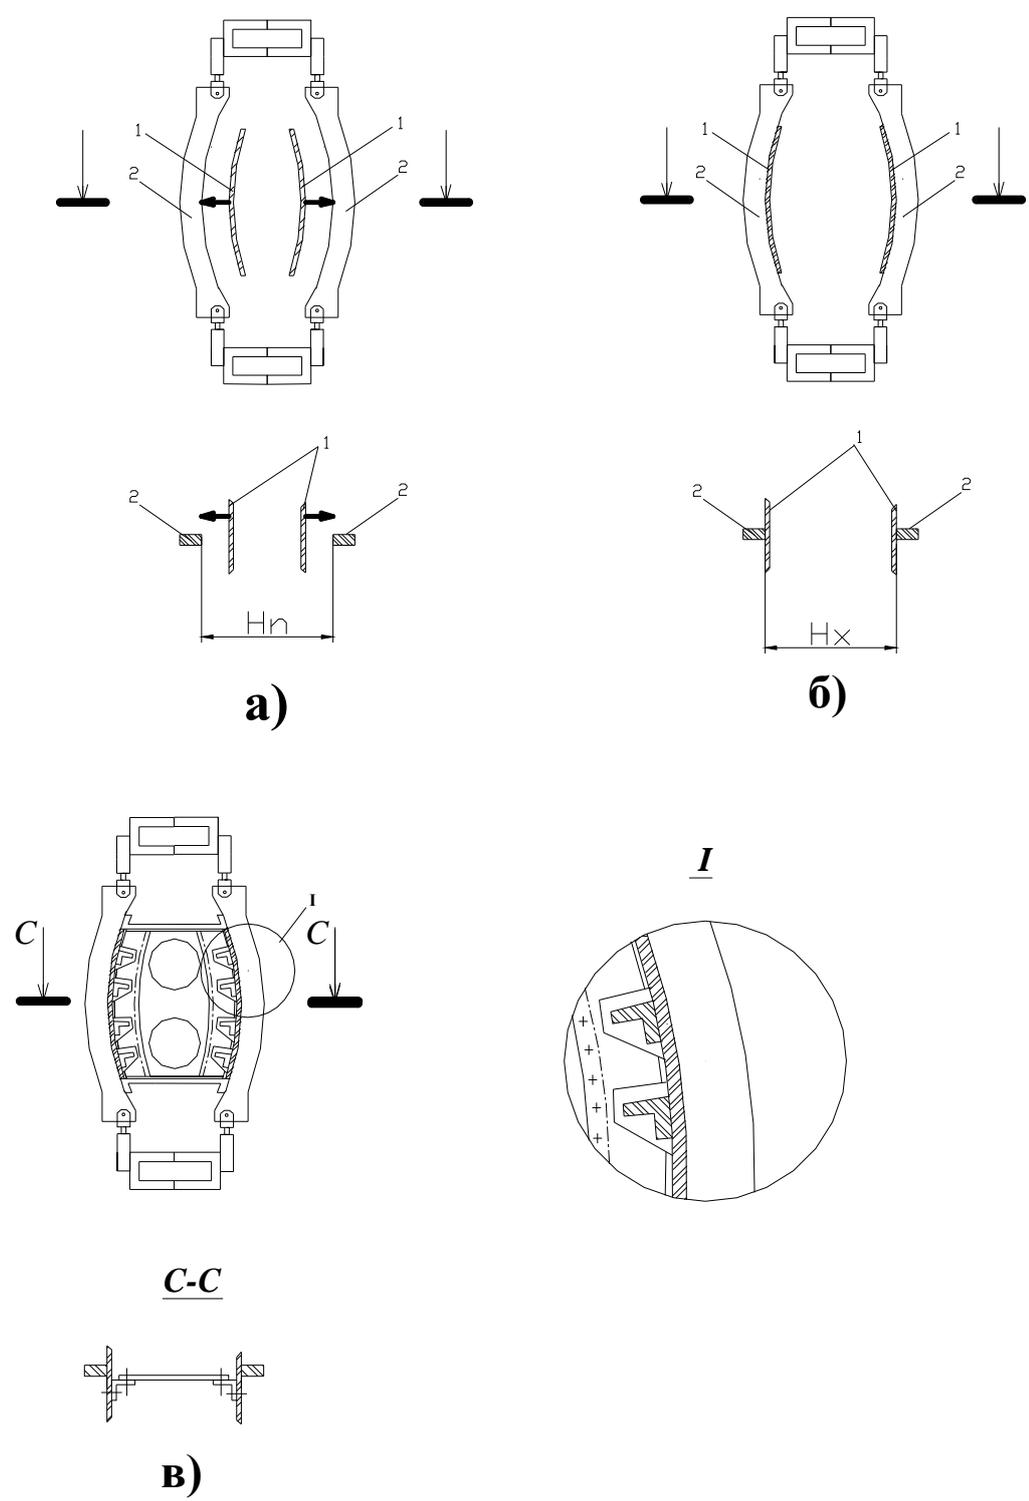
Схема сборки агрегата с базированием по наружной поверхности обшивки:
